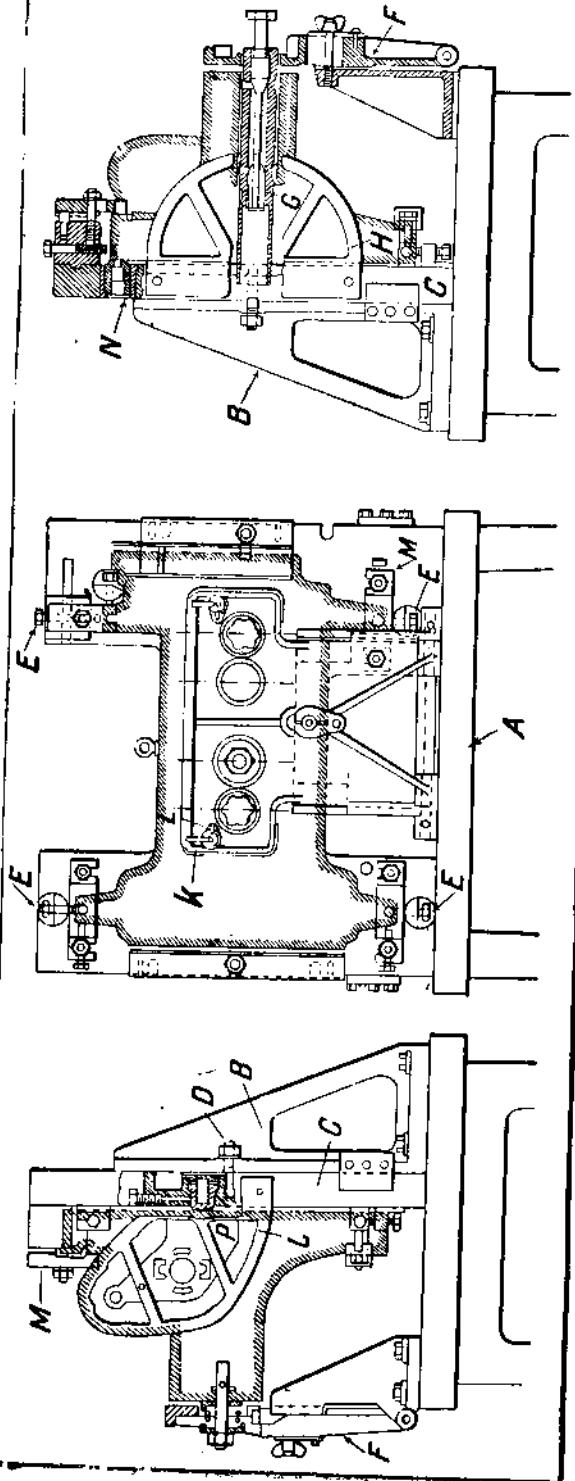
Приспособление для первой фрезерной операции по блоку Хотчкисс.
